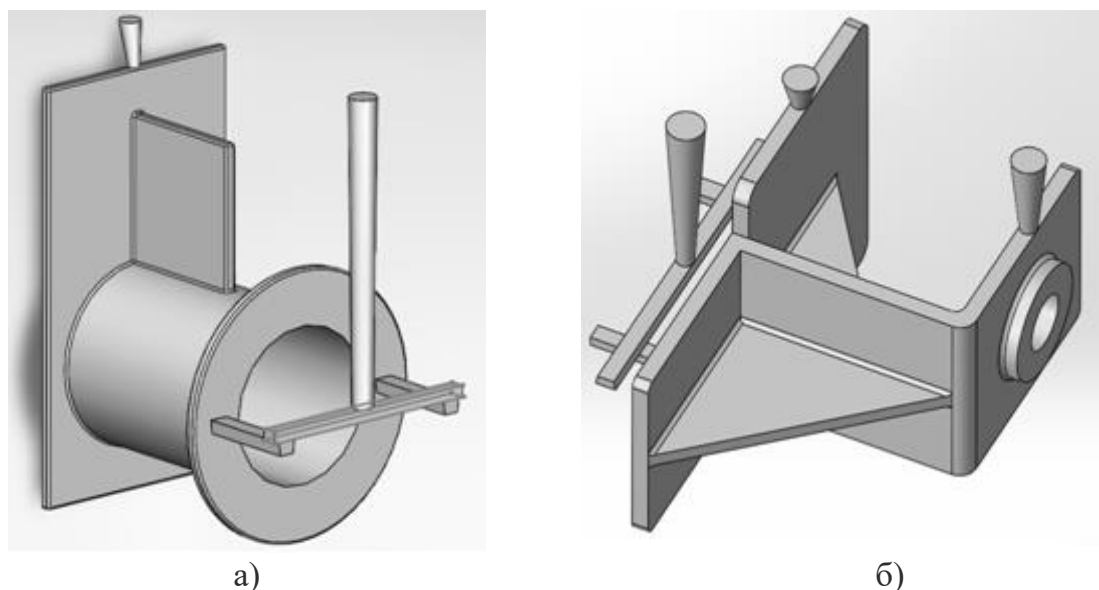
3D-модель отливки для деталей «станина» (а) и «кронштейн» (б)
